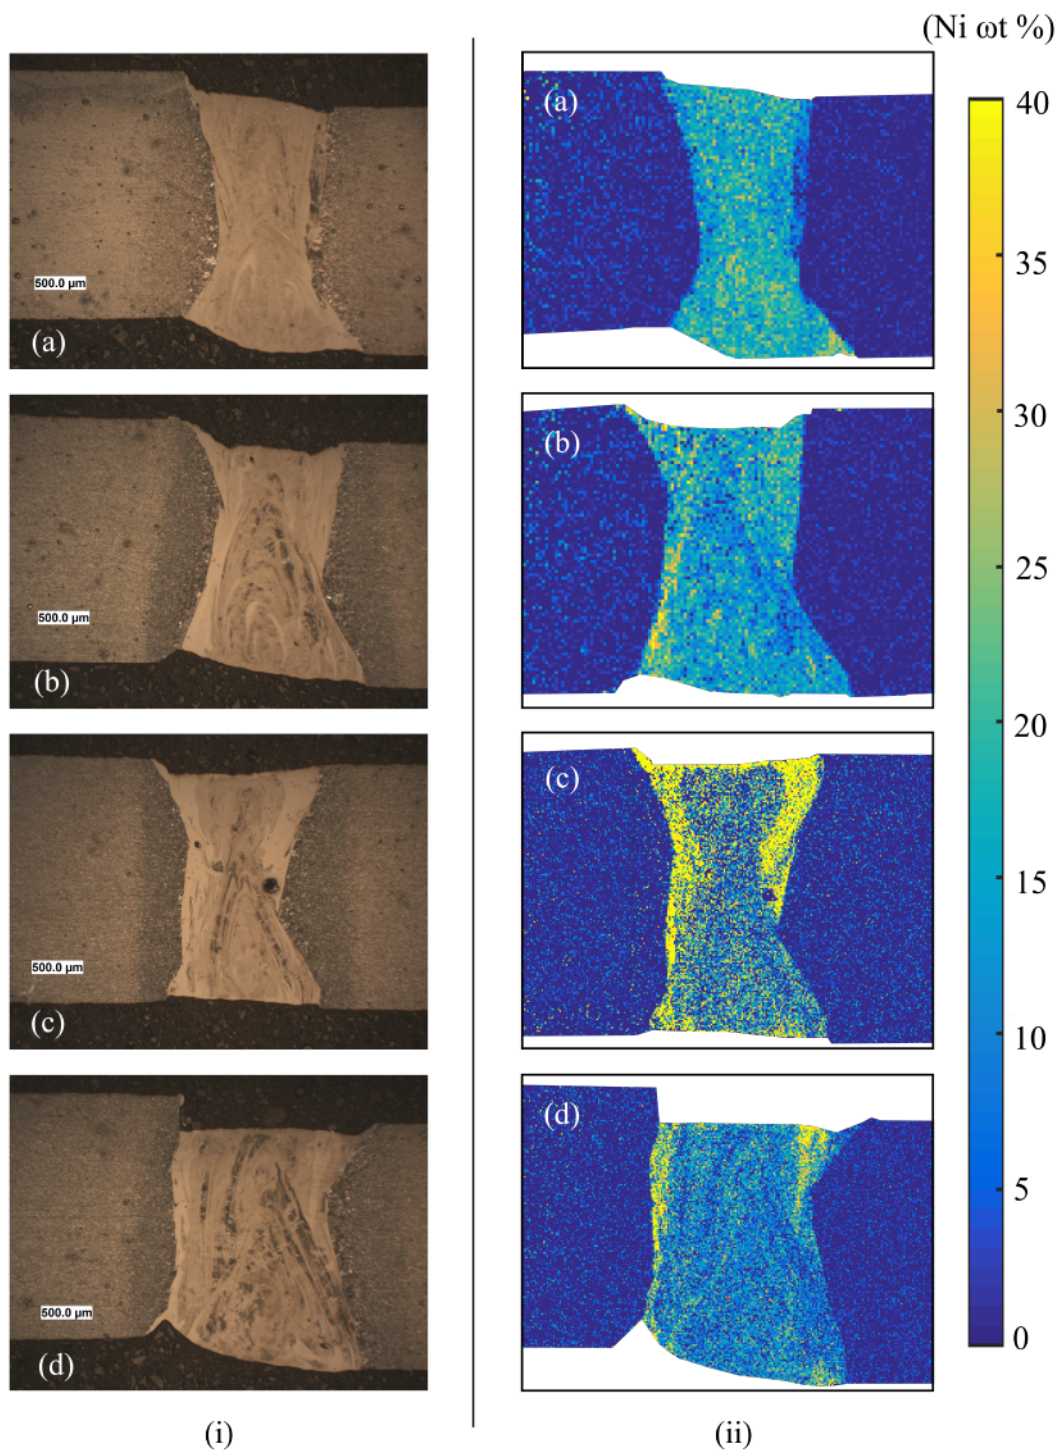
Macrographies des coupes transversales des cordons de soudure pour les configurations de soudage (a), (b), (c) et (d). (i) microscopies optiques des coupes transversales. (ii) Fraction massique en nickel (EDX).
